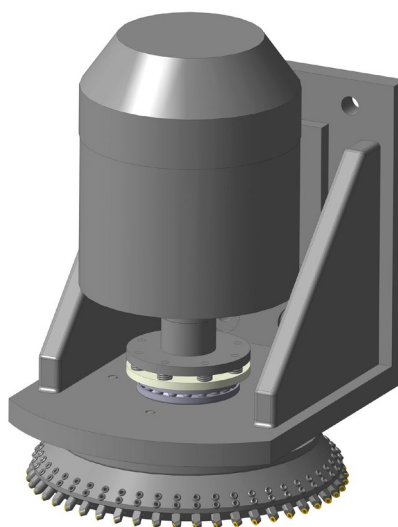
Агрегатна фрезерна головка, що містить торцеву фрезу з циліндричними різальними вставками та кріпильними гвинтами з конічними ділянками
